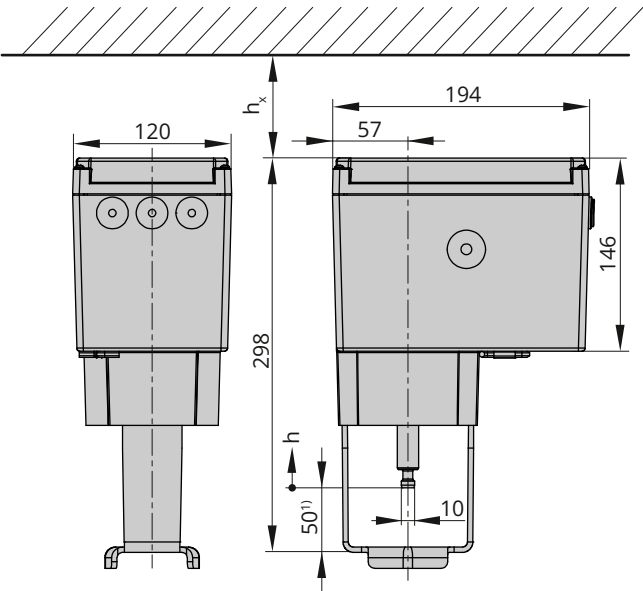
Dimensions en mm · Types 3374-10, -11, -21 et -31 (Forme B)
